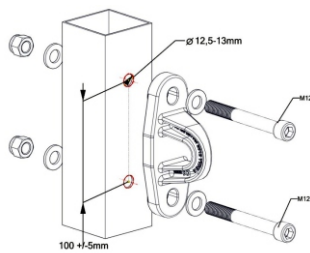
Installazione alla struttura dell'acciaio dei connettori a vite assieme al punto di ancoraggio
